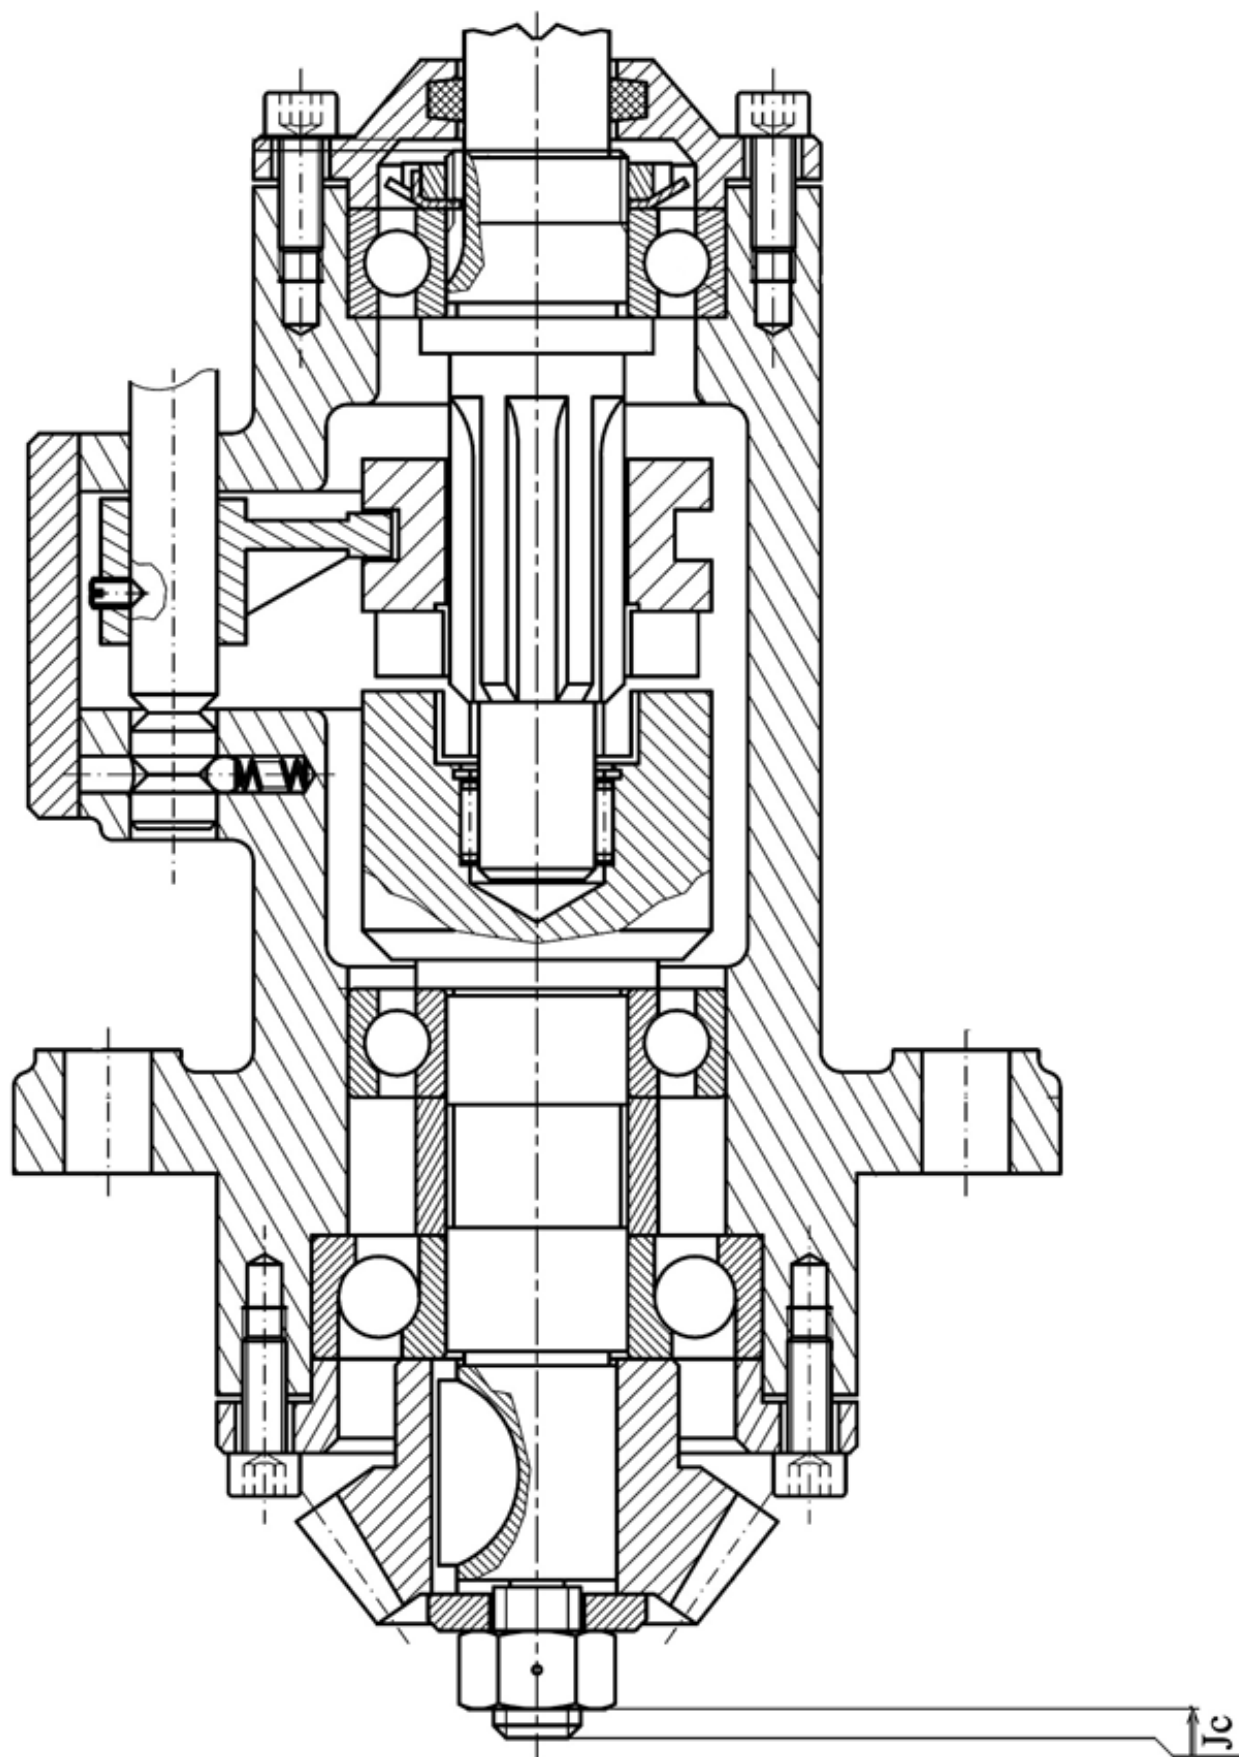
Assemblage pour la chaîne de cotes
